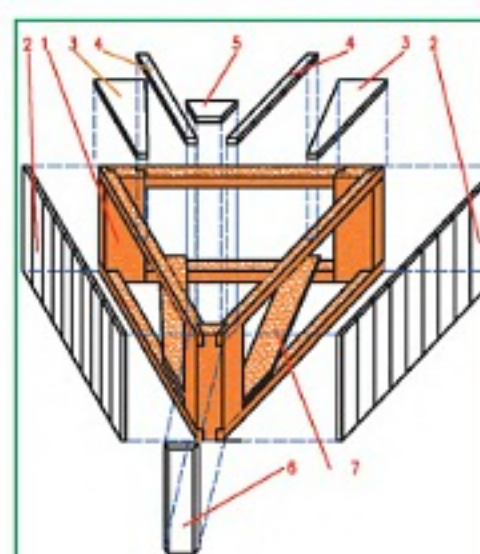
Схема сборки «трона»: 1 — каркас; 2 — боковая обшивка; 3-6 — накладки; 7 — дно.
